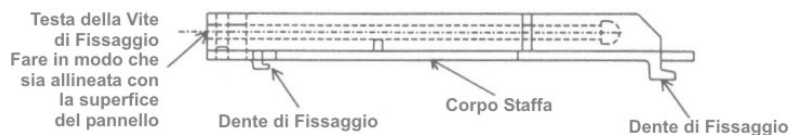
Staffa di Fissaggio Vista Lateralmente
